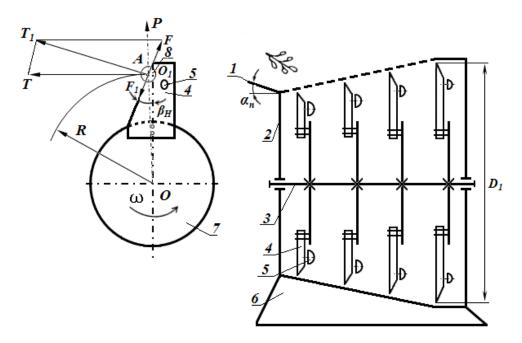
Схема мини-измельчителя для грубых кормов: 1-лоток; 2-кожух; 3-вал с дисковом ротором; 4-нож; 5-грузок; 6-подставке; 7-ротор; 8-стебель
